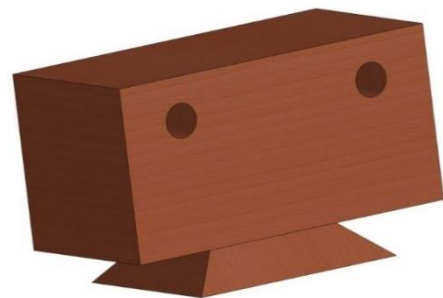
Design 3D pour Pièce côté gauche de curseur
